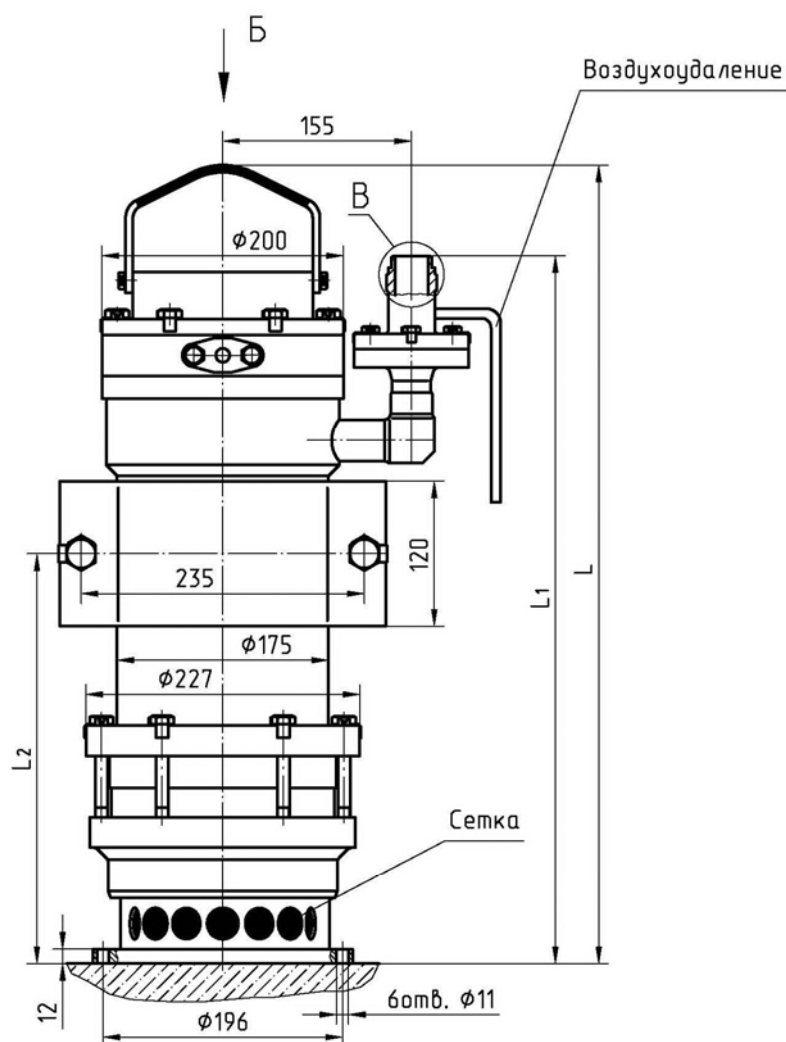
Габаритный чертеж насоса бака сбора отмывочных вод
